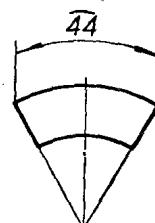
11 光滑过渡处尺寸界线、尺寸线的画法
